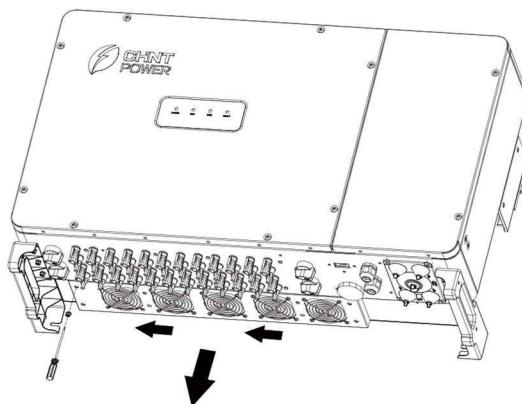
Remova a bandeja do ventilador e o ventilador
